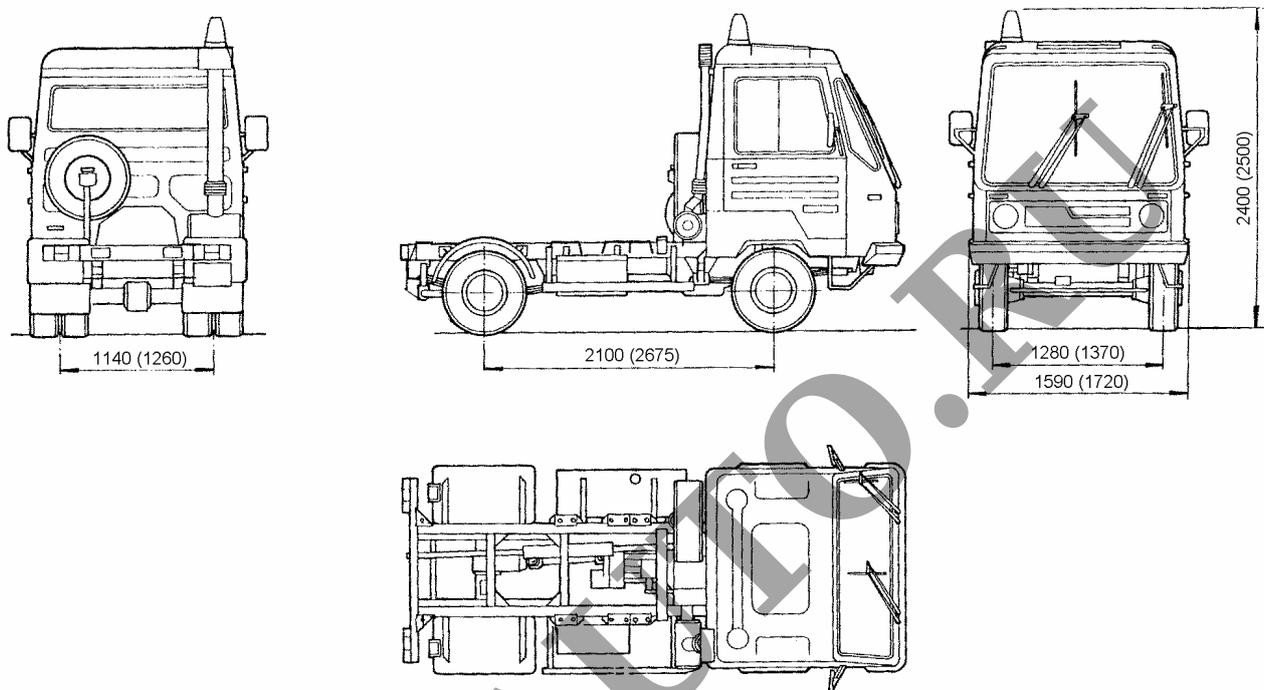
Автомобиль Multicar M26.5 без навесного оборудования (с кронштейнами крепления)
